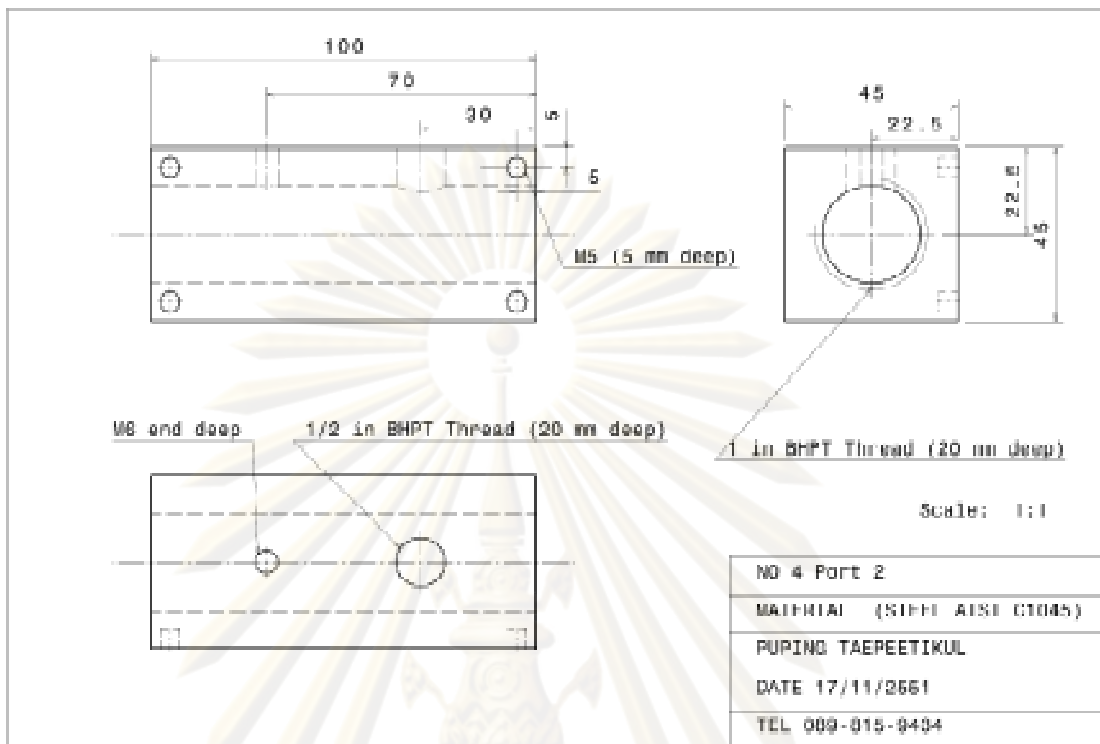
แบบ Drawing ของ Port valve 1
